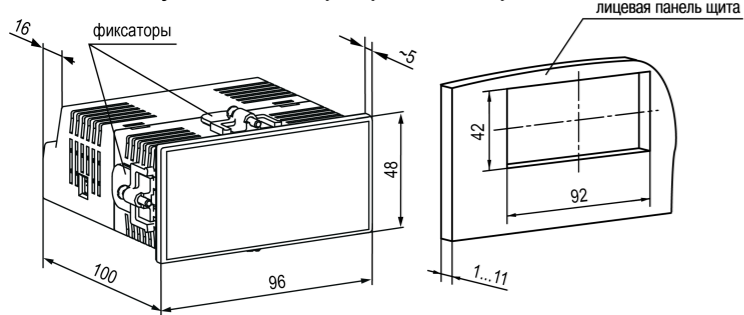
Габаритные размеры корпуса Щ2 и монтажного отверстия в щите
